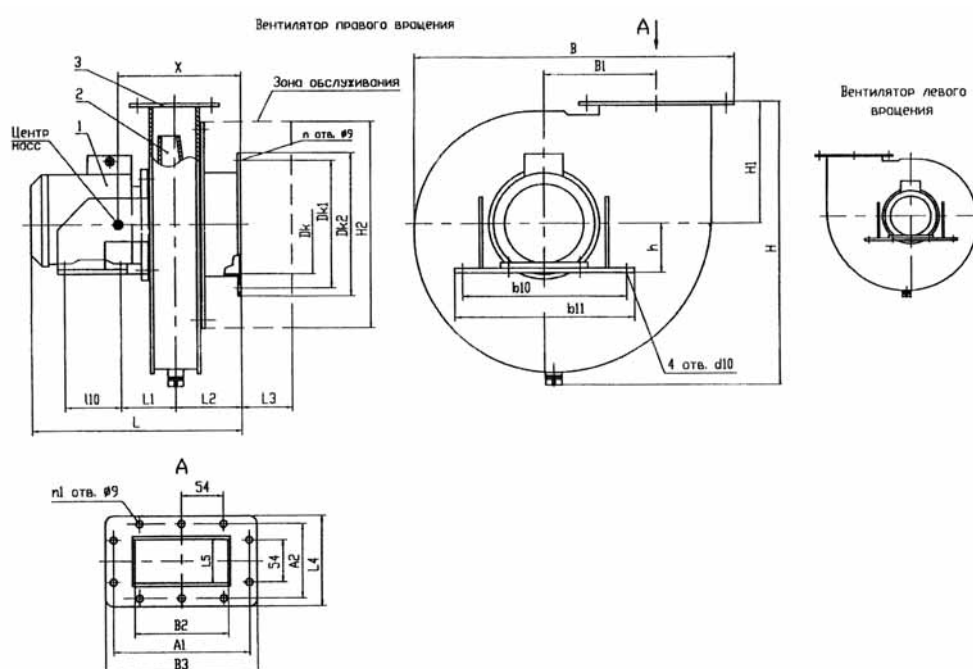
1 – двигатель; 2 – колесо рабочее; 3 – корпус
